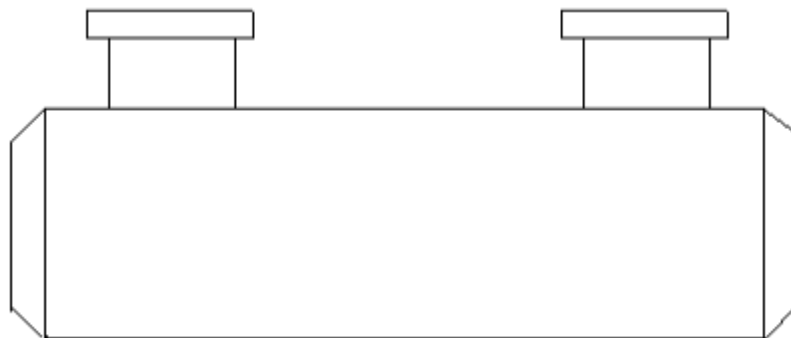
Общий вид резервуара стального горизонтального цилиндрического 607-ЕПП16-00.000
